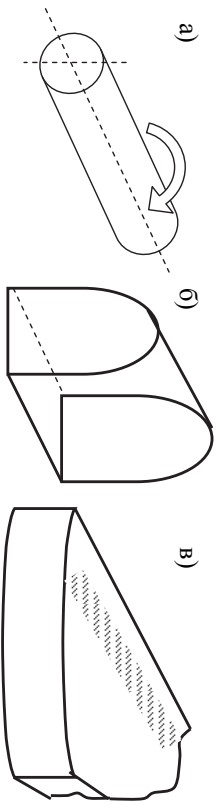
Формы оснасток для изготовления изделий из ПКМ: а – оправка; б – болванка; в – форма
